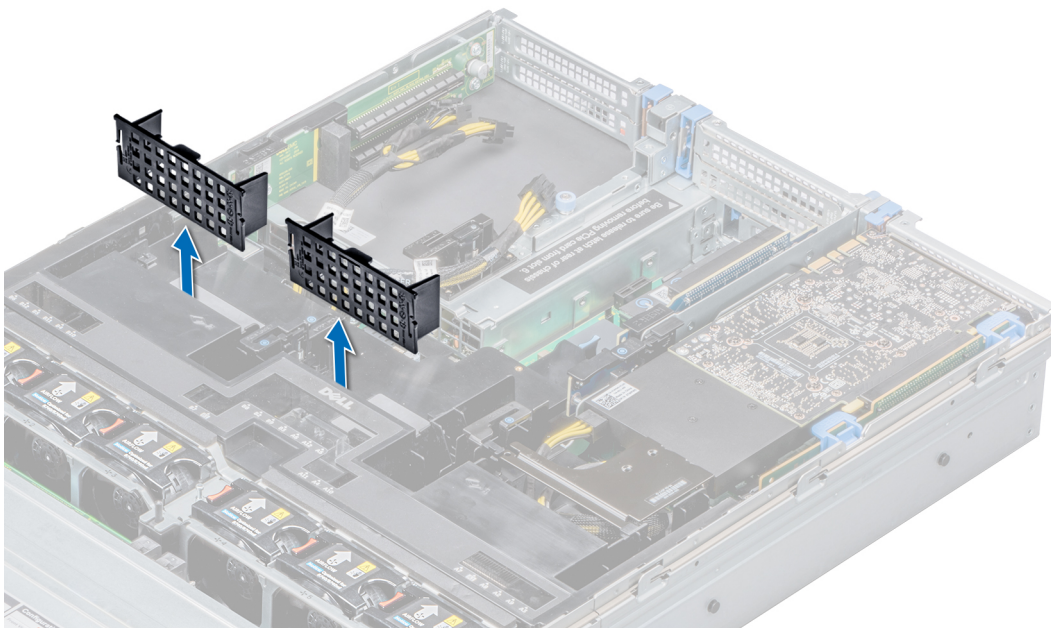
Obere Abdeckung des Kühlgehäuses entfernen
